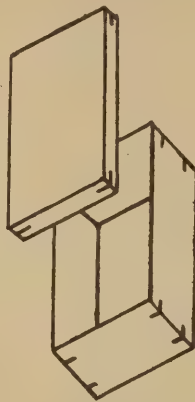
Schachtel mit Drahtheftung und Stoßecken.
